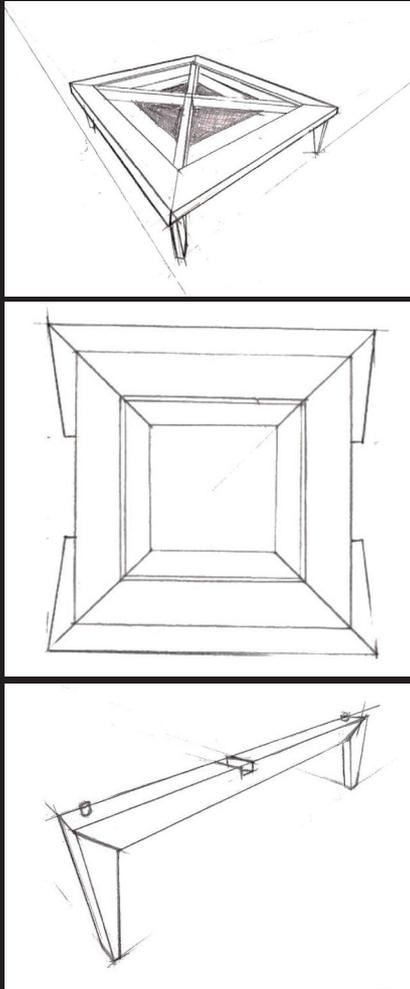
Sketches manuais com a definição tridimensional do conjunto, a planificação dos componentes e o detalhamento dos encaixes entre as peças.
